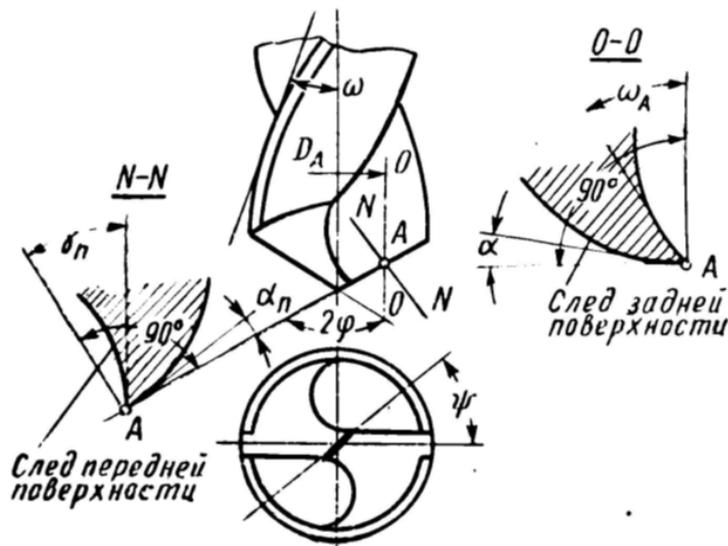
Геометрические параметры режущей части спирального сверла
